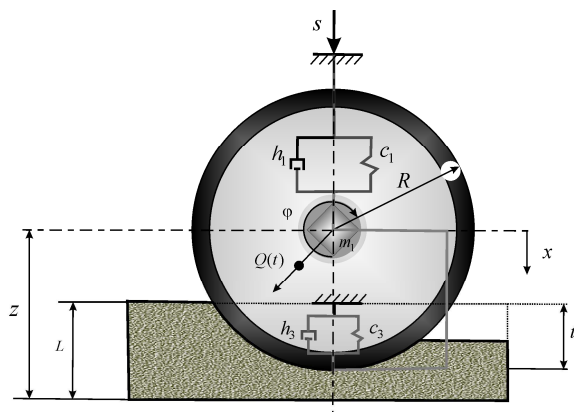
Эквивалентная схема динамической системы плоскошлифовального станка
